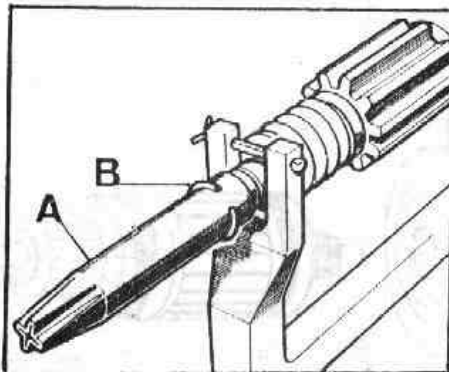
Montaje del conjunto de muelles y engranajes en el eje del inducido
